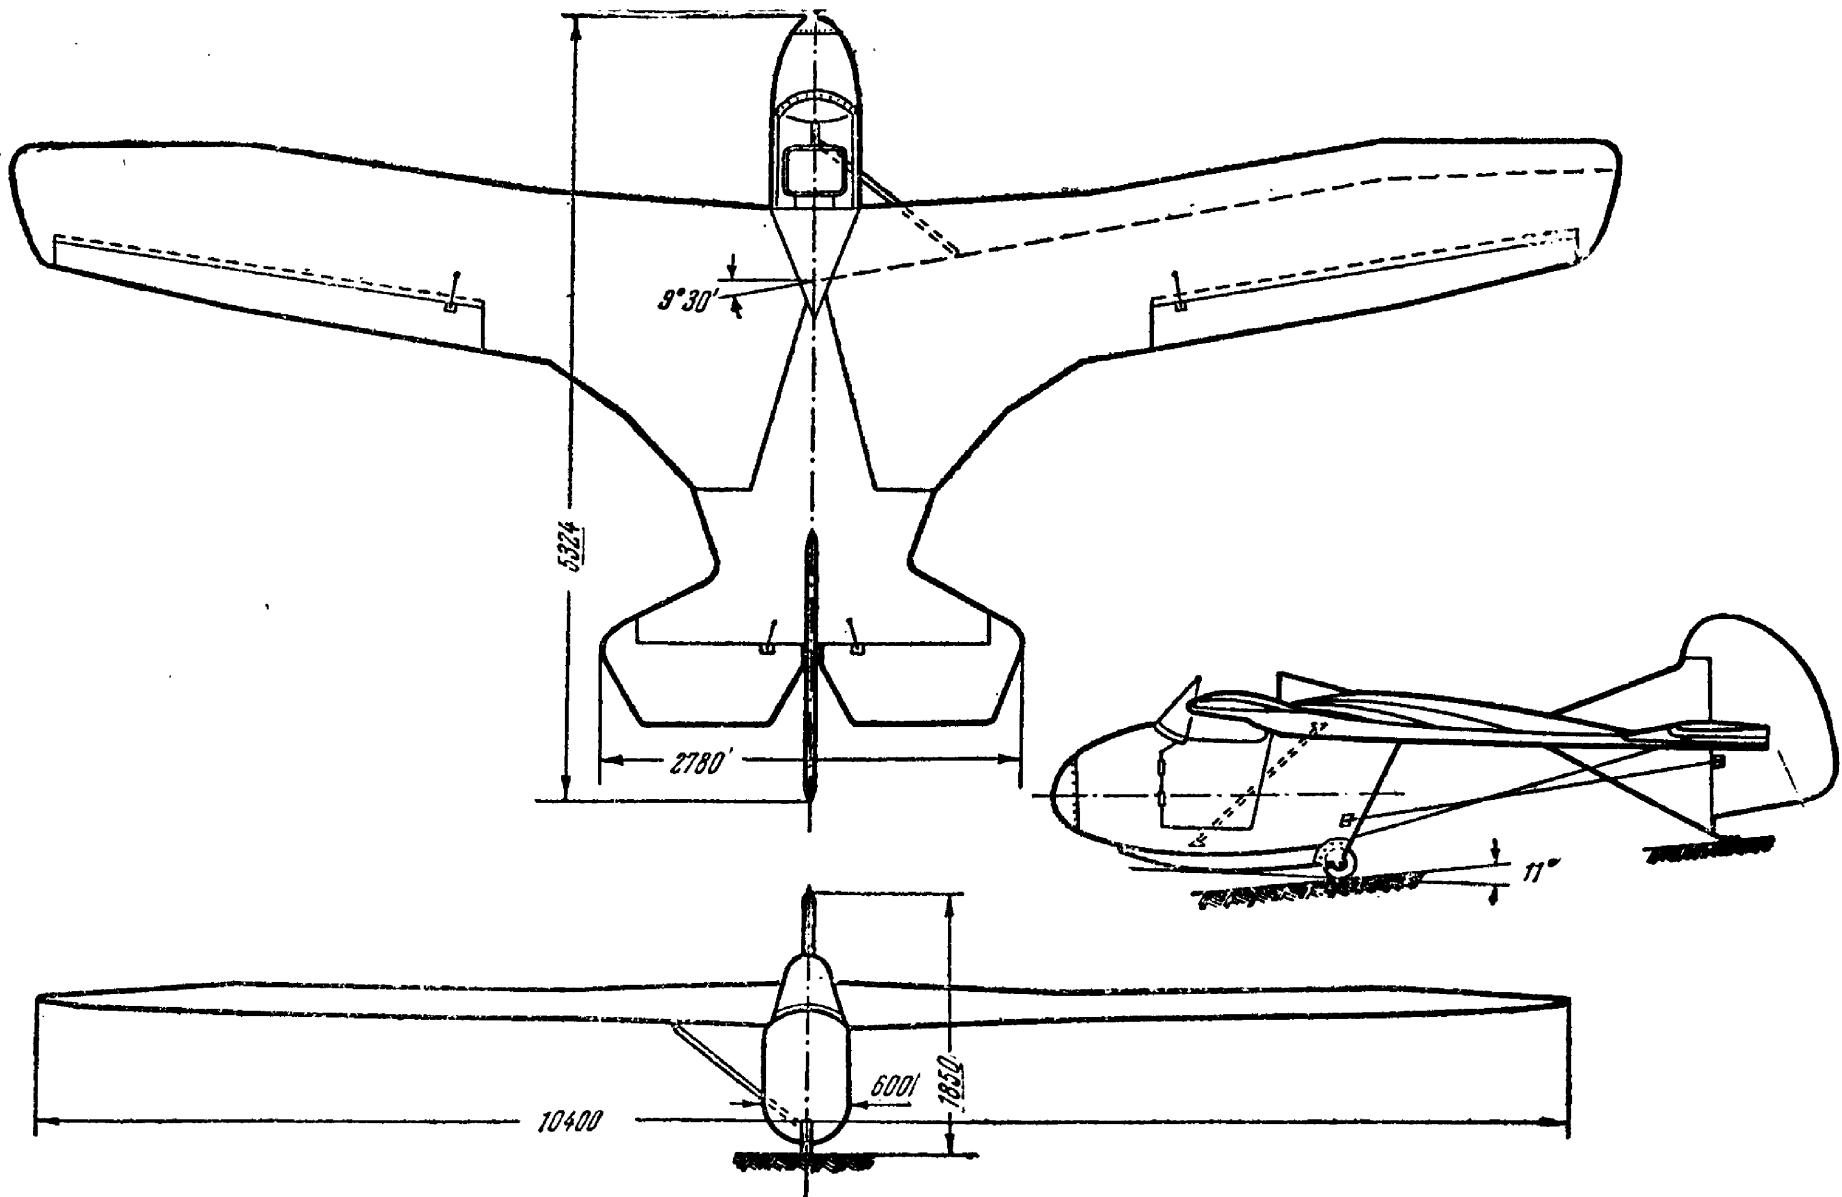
Схема планера MAK-15 конструкции М. А. Кузакова
